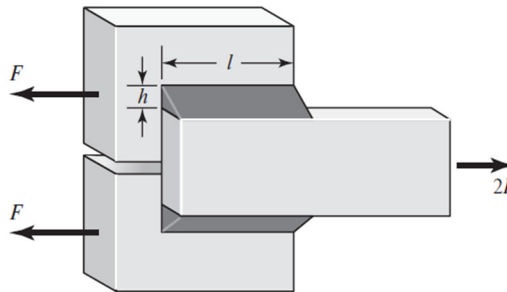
Soldadura de filete paralelas. [24]
